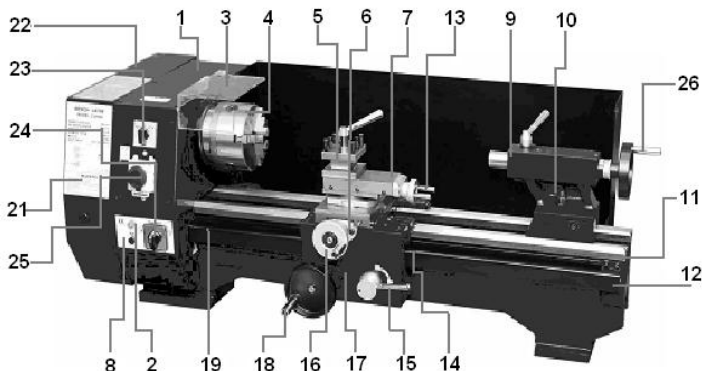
Общий вид токарного станка MCJ 250/400-1.
